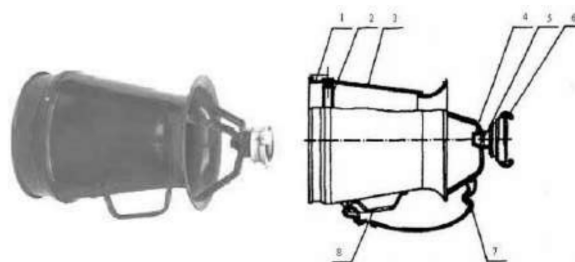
Будова генератора піни середньої кратності ГПС-600: 1 – насадок; 2 – касета сіток; 3 – корпус генератора; 4 – корпус розпилювача; 5 – розпилювач; 6 – з'єднувальна головка ГМ-70; 7 – ремінь; 8 – ручка для перенесення
